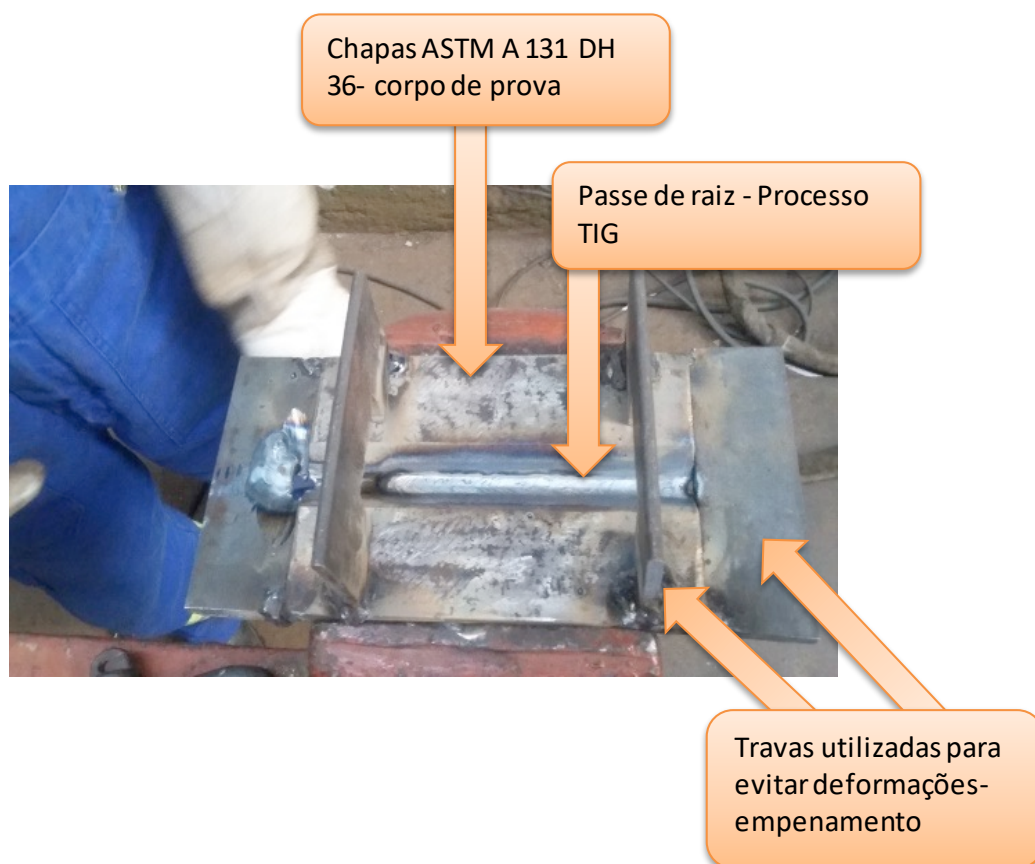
Corpo de prova durante soldagem TIG. Fonte: autor (2019)
